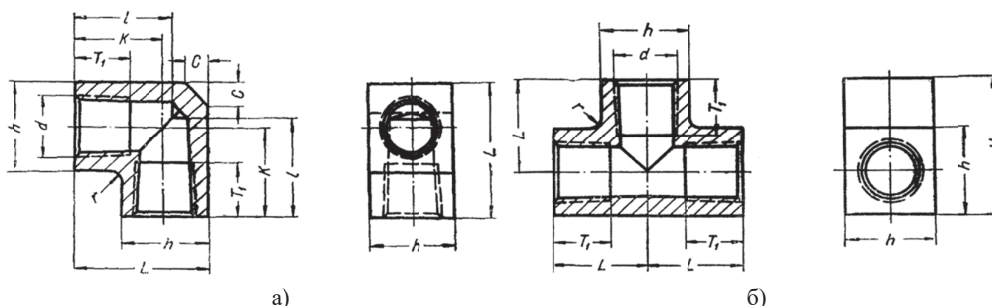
Фитинги для резьбовых соединений с трубной конической резьбой по ГОСТ 6111-52:
